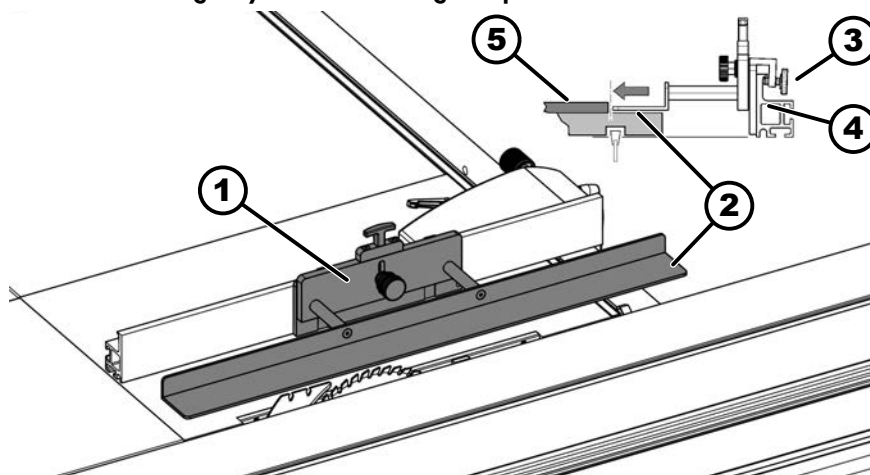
Montage de la butée auxiliaire "Sägeboy"
